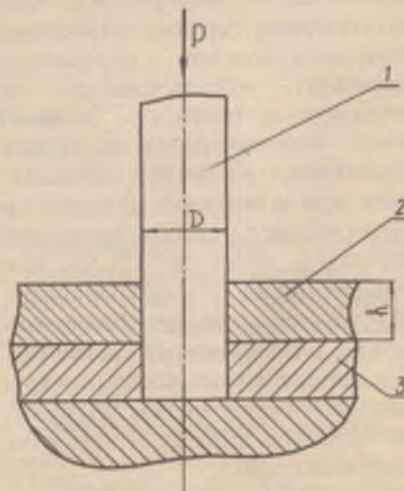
Схема прошивки отверстий: 1 — пуансон; 2 — заготовка решетки; 3 — матрица штампа
